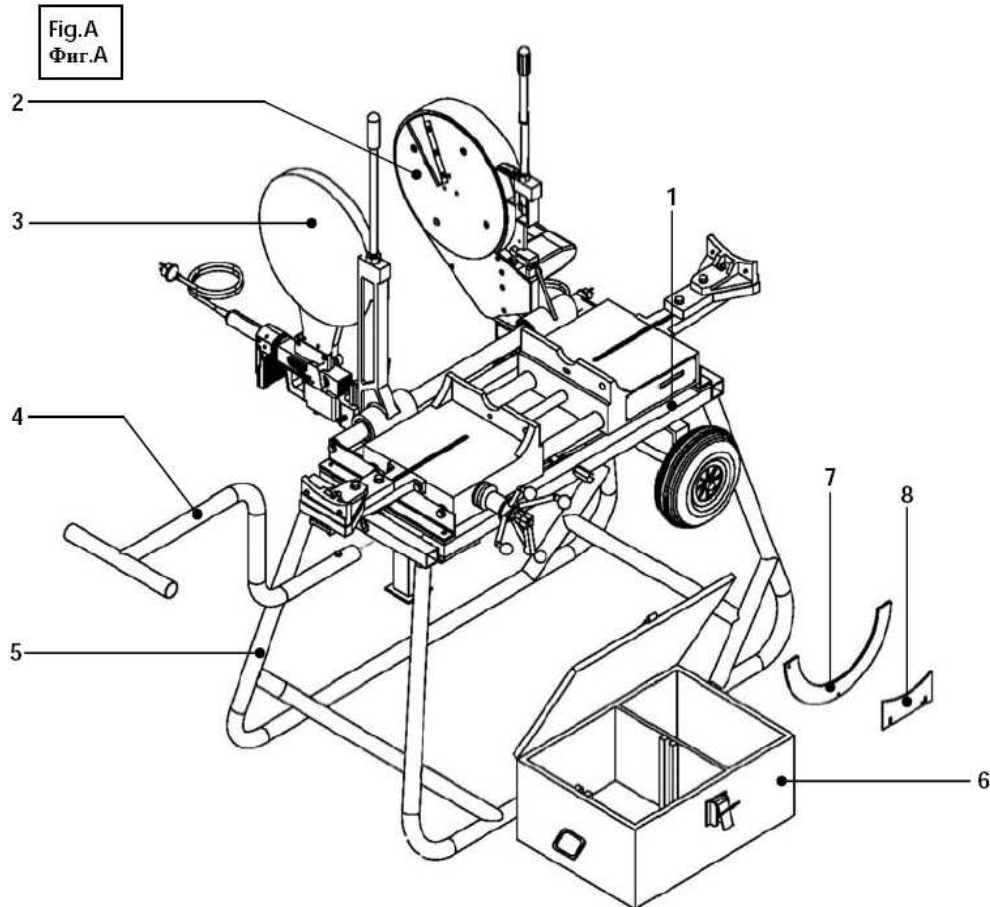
baza, 2- freza, 3- termopaca, 4- maneta, 5- cadru, 6- cutie, 7 bac 8- adaptor
